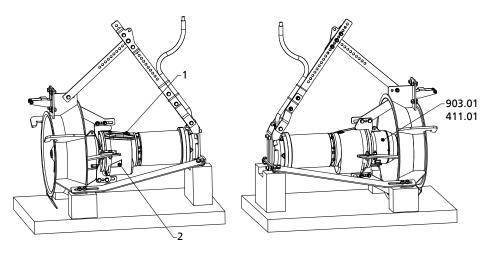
Llenado del líquido lubricante; Amaline 500, 600, 800
